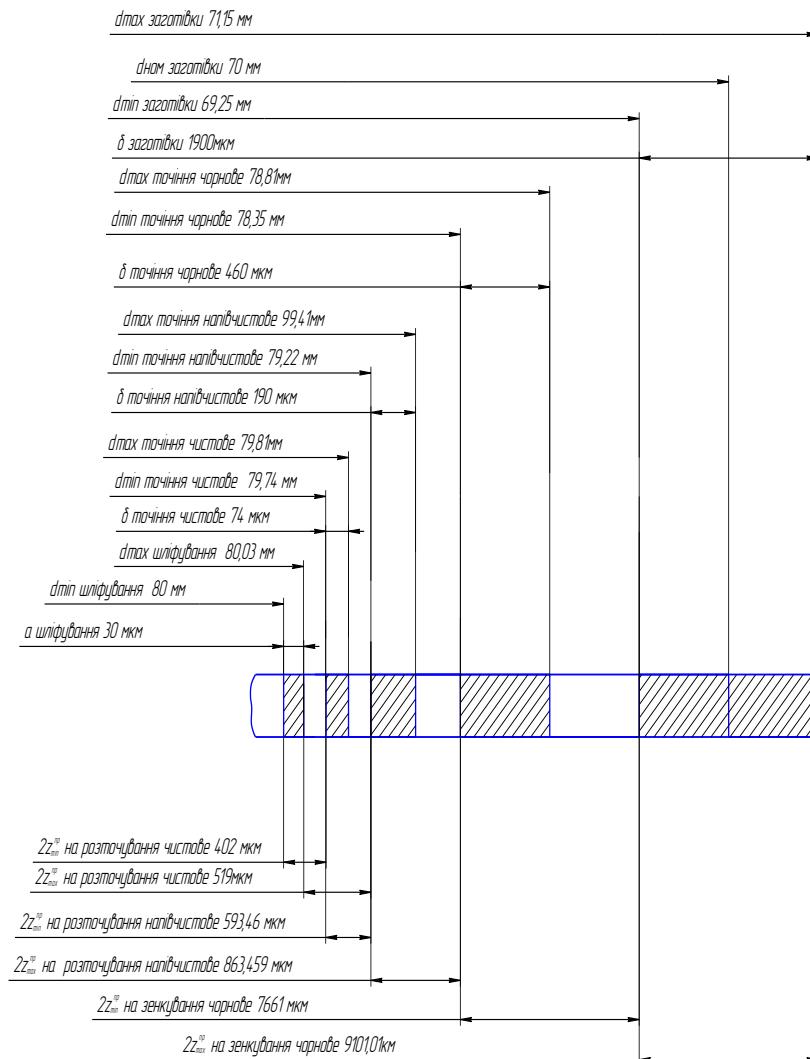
Схема графічного розташування припусків і допусків на обробку зовнішньої поверхні
